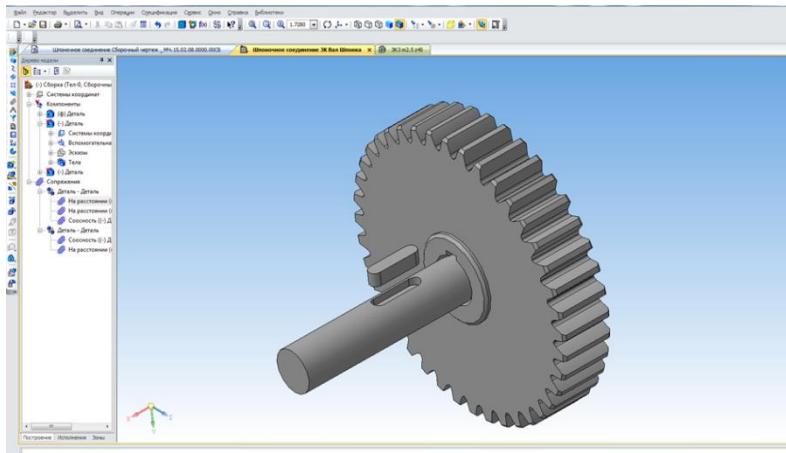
Демонтарция зубчатого колеса, вала и шпонки в КОМПАС
